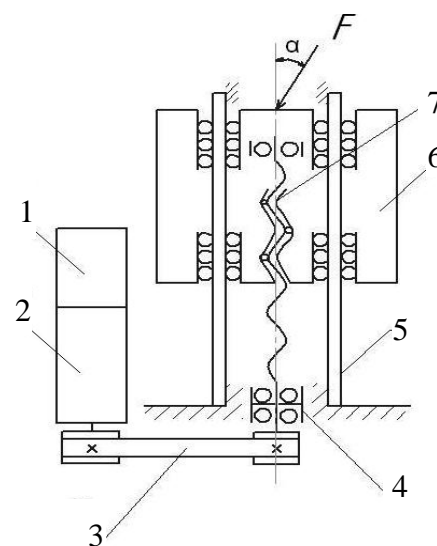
Привод вертикального перемещения: 1 – датчик; 2 – мотор; 3 – зубчатый ремень; 4 – подшипник; 5 – линейные роликовые направляющие; 6 – подъемный стол; 7 – ШВП
